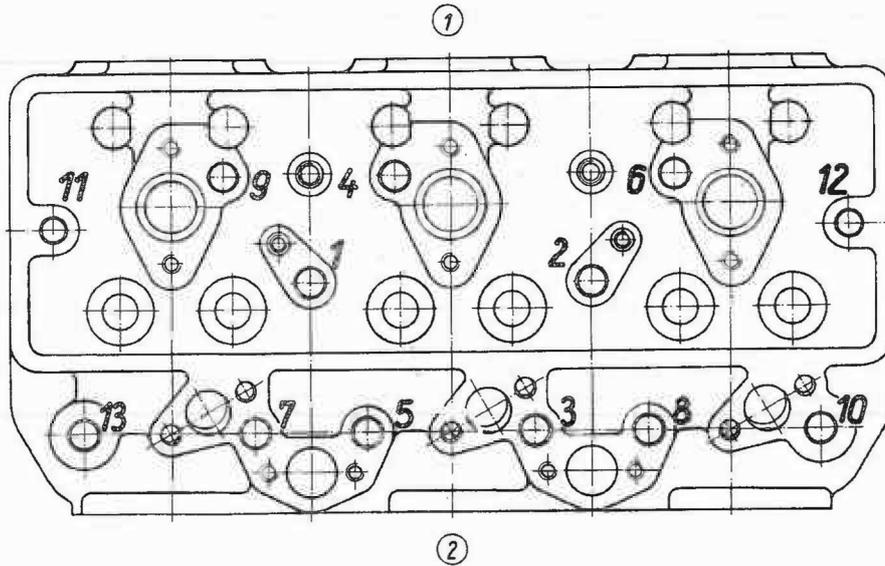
Schema für das Anziehen der Muttern zur Befestigung des Zylinderkopfes
